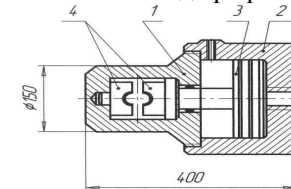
Конструктивна схема силової головки гідравлічного преса: 1 – корпус, 2 – циліндр, 3 – поршень, 4 – профільні пуанسونи.
